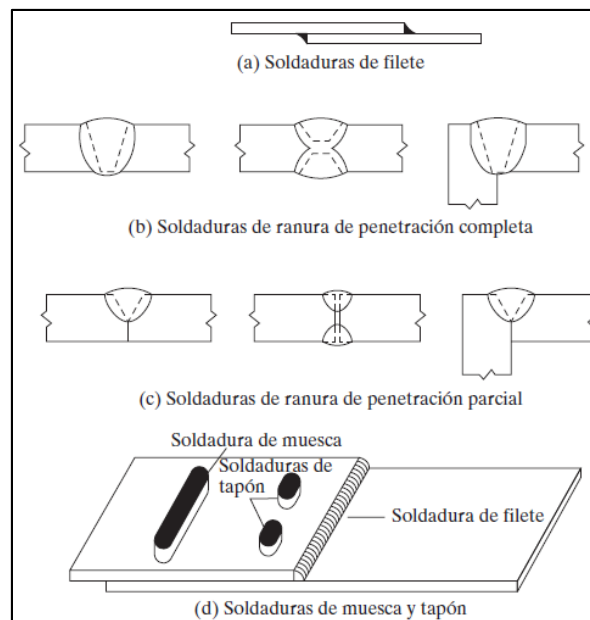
Cuatro diferentes tipos de soldaduras estructurales.
